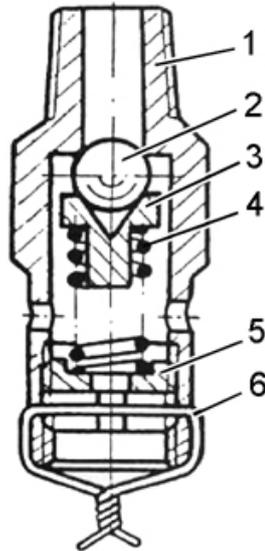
Установка на корпус крепления шестеренного насоса ГС трансмиссии, механизма включения привода насоса, предохранительного клапана
